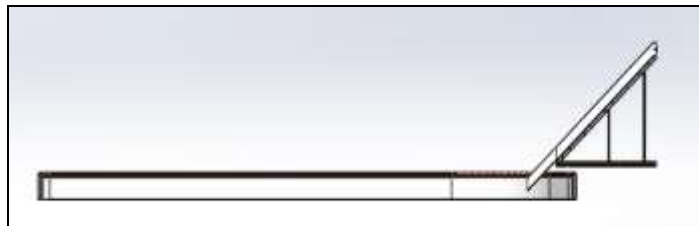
Ensamble del sistema filtrado y transporte vista alzada
